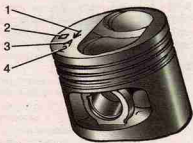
Маркировка поршня: 1 – стрелка для ориентирования поршня в цилиндре; 2 – ремонтный размер; 3 – класс поршня; 4 – класс отверстия для поршневого пальца
